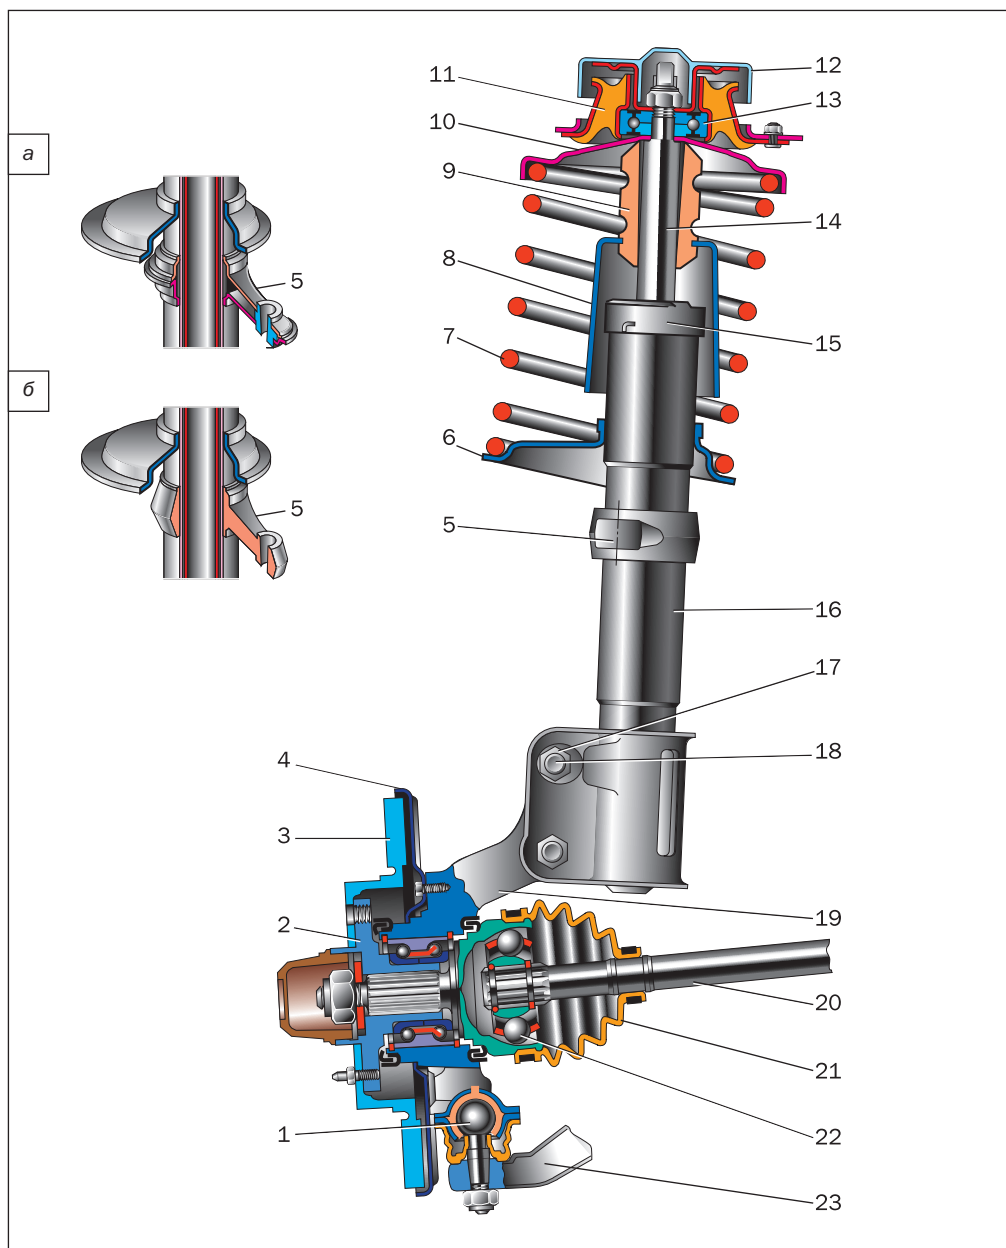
Передняя подвеска автомобиля ВАЗ-2109: 1 — шаровая опора; 2 — ступица; 3 — тормозной диск; 4 — защитный кожух; 5 — поворотный кулак; 6 — нижняя опорная чашка; 7 — пружина подвески; 8 — защитный кожух; 9 — буфер сжатия; 10 — верхняя опорная чашка; 11 — резиновый элемент верхней опоры; 12 — защитный колпак; 13 — подшипник верхней опоры; 14 — шток; 15 — опора буфера сжатия; 16 — телескопическая стойка; 17 — гайка; 18 — эксцентриковый болт; 19 — поворотный кулак; 20 — вал привода переднего колеса; 21 — защитный чехол шарнира; 22 — наружный шарнир вала; 23 — нижний рычаг; а — стойка с полым поворотным рычагом; б — стойка с цельнометаллическим поворотным рычагом
